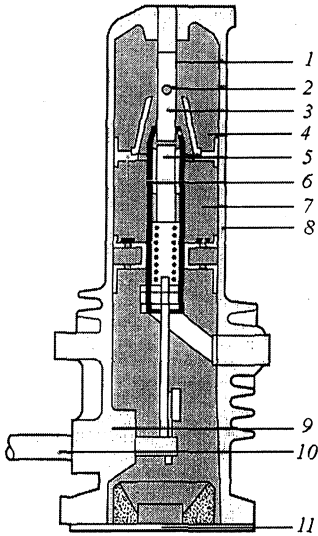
Полюс выключателя: 1 — корпус; 2 — изолирующее сопло; 3 — неподвижный дугогасительный контакт; 4 — главный подвижный контакт; 5 — подвижный дугогасительный контакт; 6 — подвижный поршень; 7 — камера сжатия; 8 — клапаны; 9 — система уплотнения; 10 — вал привода; 11 — нижняя крышка
